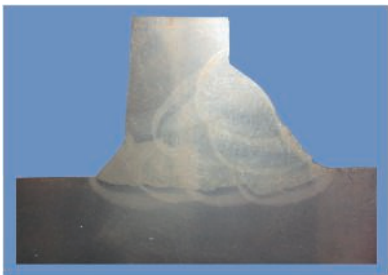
Mit Schweißspaltklammer geschweißter Vollanschluss am T-Stoß mit ausgeprägter Abflachung der Nahtwurzel.
